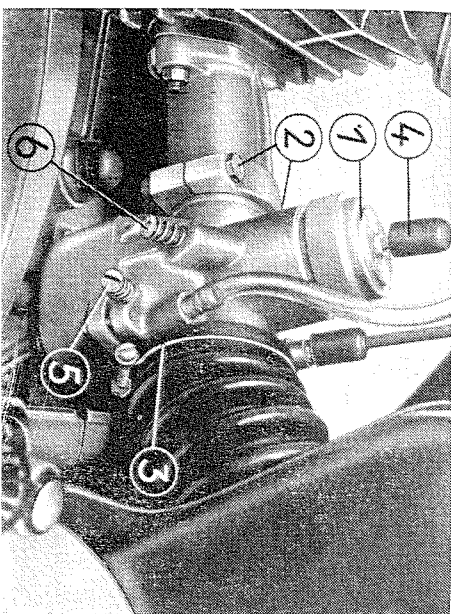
Déposer le carburateur 30 N 2-3 (T.S. 250 I)
